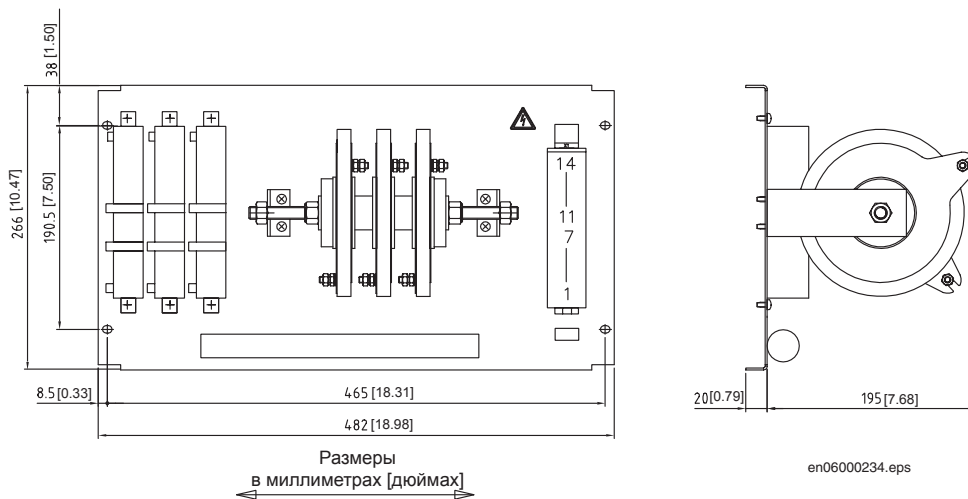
Габаритный чертеж трехфазного резисторного блока
